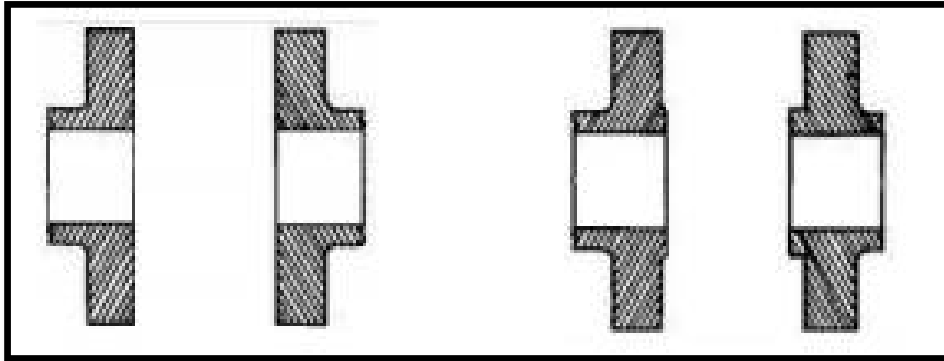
Brida FF -Flat Face- a la izquierda y brida RF -Raised fac-e a la derecha
